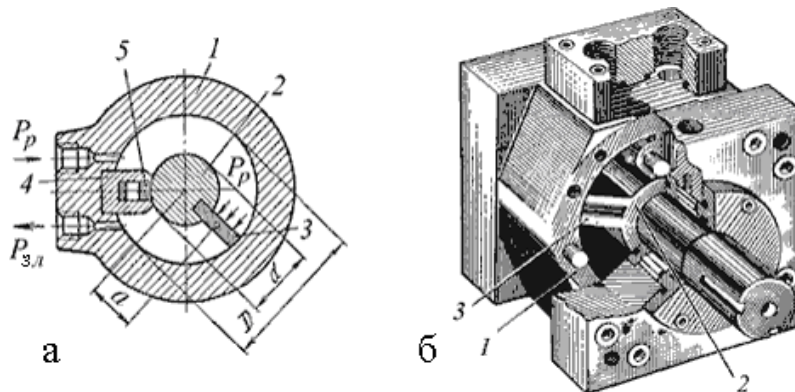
Поворотний однолопатевий гідроциліндр
